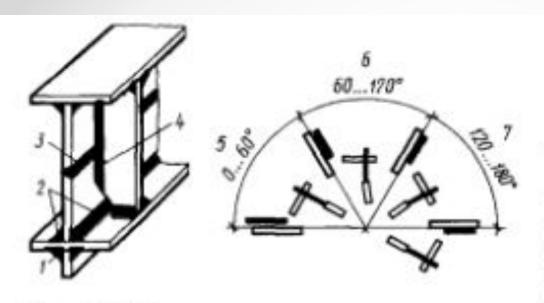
Положение швов в пространстве: — потолочный угловой шов; 2— нижний угловой шов «в лодочку»; 3— горизонтальный стыковой шов; 4— вертикальный угловой шов; 5. 6. 7— нижние, вертикальные и потолочные швы
